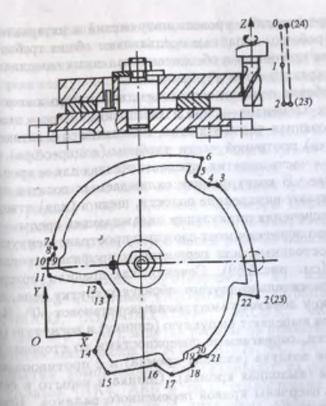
Схема фрезерования контура кулачка на станке с ЧПУ
